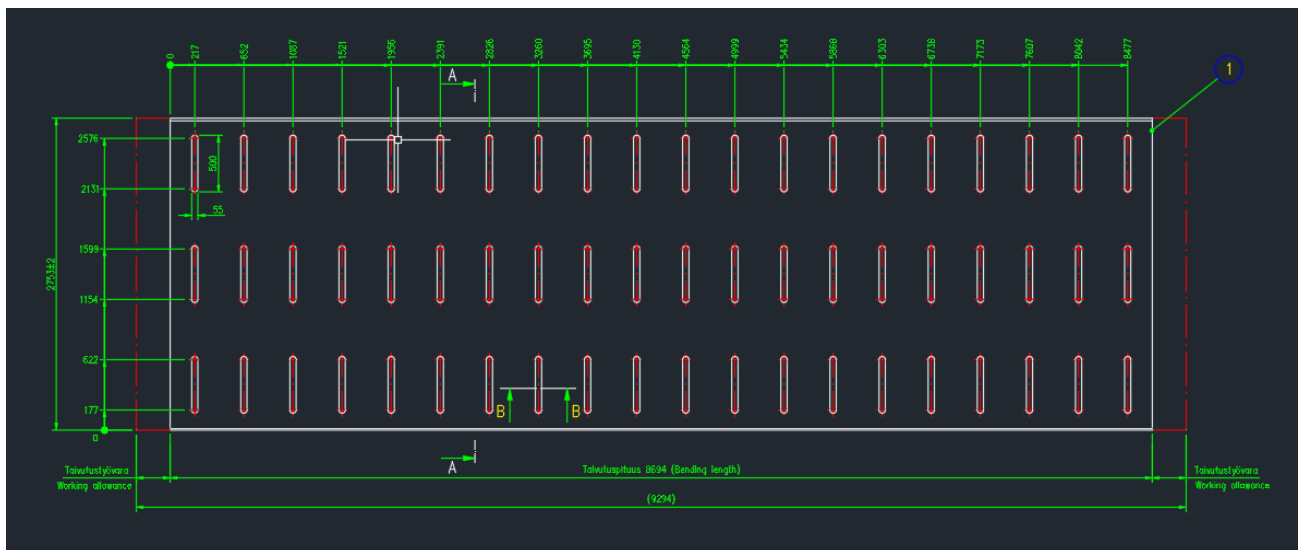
Plano de plancha sección 1 descortezador [Andritz]
